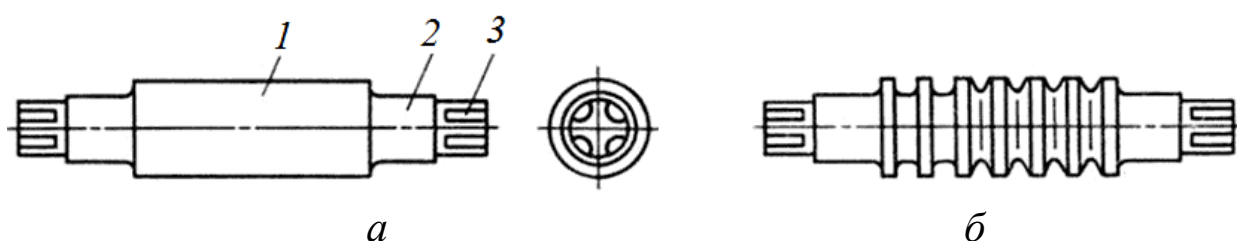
Прокатные валки: а – гладкий; б – калиброванный
